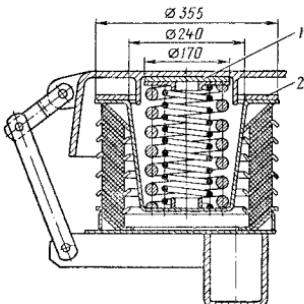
Регулировка центрального люлечного подвешивания прокладками
